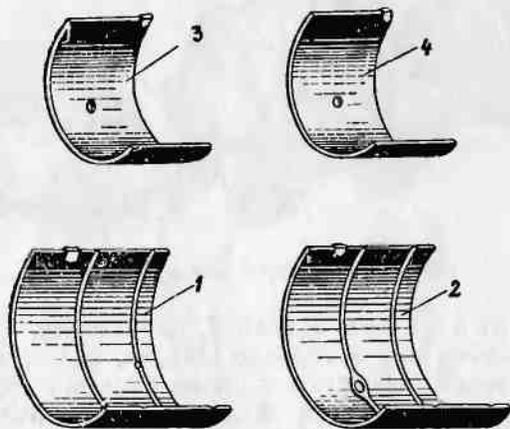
Биметаллические вкладыши подшипников коленчатого вала двигателя:
